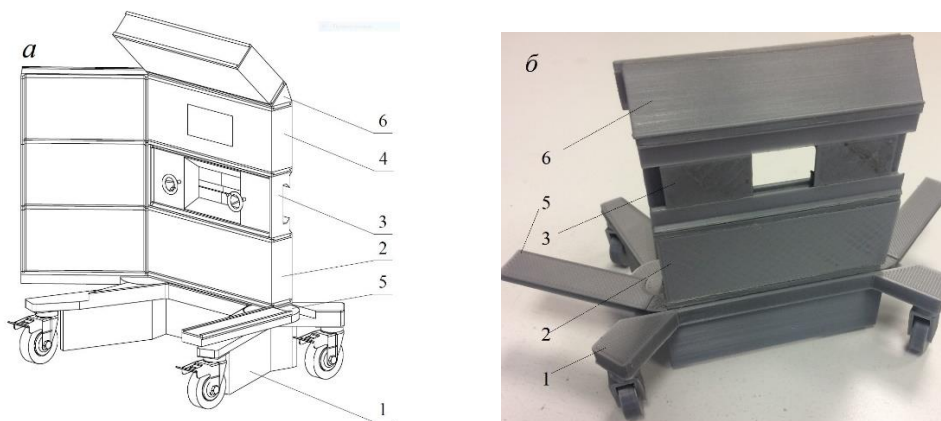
Чертеж (а) и 3D-модель (б) сборной мобильной биологической защиты: 1 – основание; 2 – основные блоки; 3 – блок с защитными шторками; 4 – блок с защитным стеклом; 5 – поворотные консоли для боковой защиты; 6 – переходные элементы
